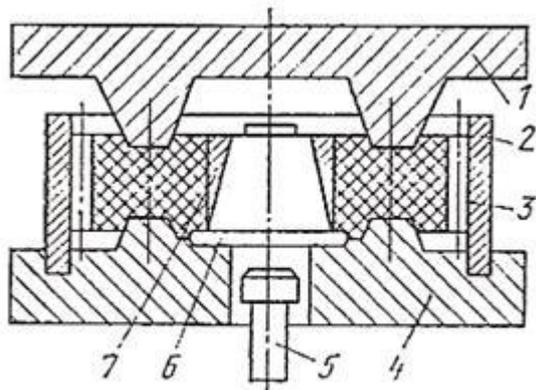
Принципиальная схема штампа для восстановления шестерен способом пластического деформирования: 1 — пуансон; 2 — ограничительное кольцо; 3 — шестерня; 4 - матрица; 5 — выбрасыватель; 6 — центрирующий конический вкладыш; 7 — разрезанная коническая пружинящая втулка
